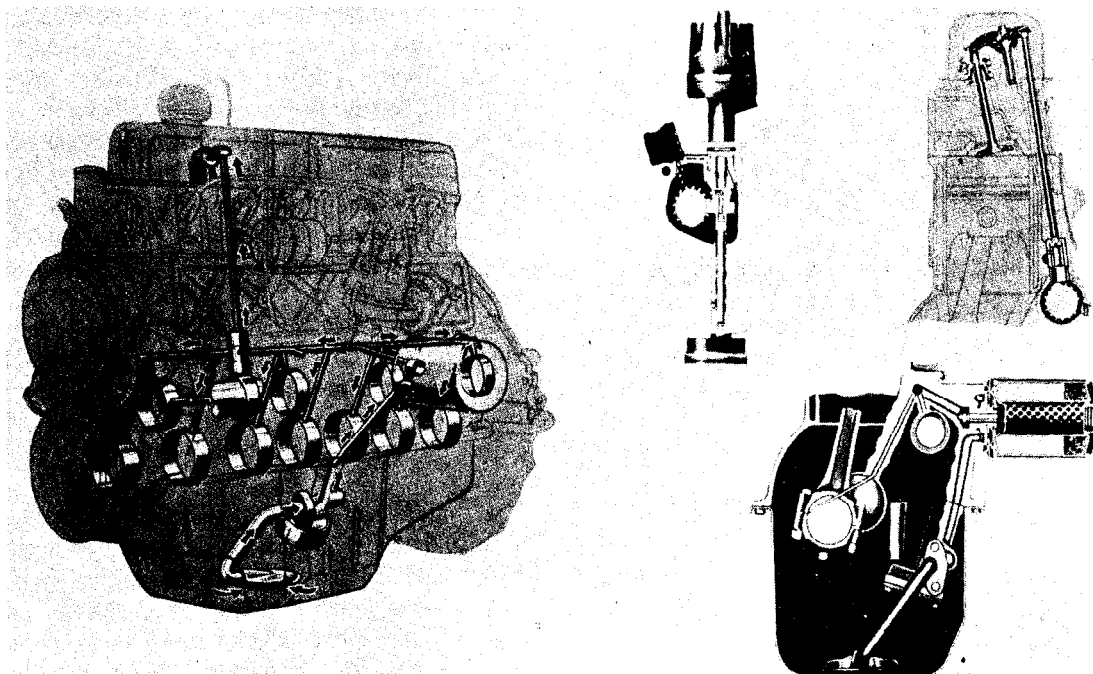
Sistema de engrase de un motor de 6 cilindros, con válvulas en cabeza y 7 cojinetes en el cigüeñal (*Ford Division of Ford Motor Company*).
